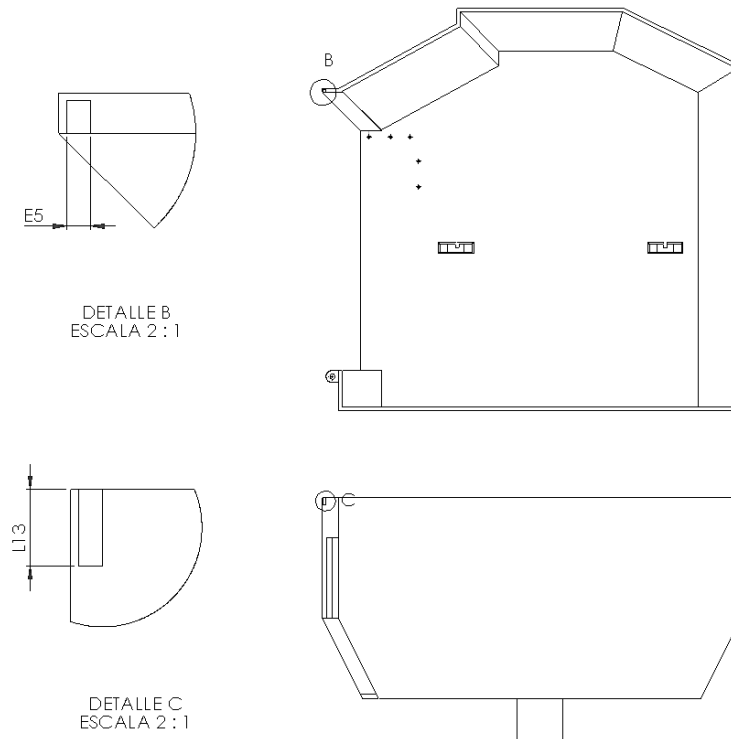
Croquis de dimensions. Elemento 1.1.1.1.2.
